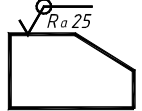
Обозначение шероховатости, одинаковой по контуру
